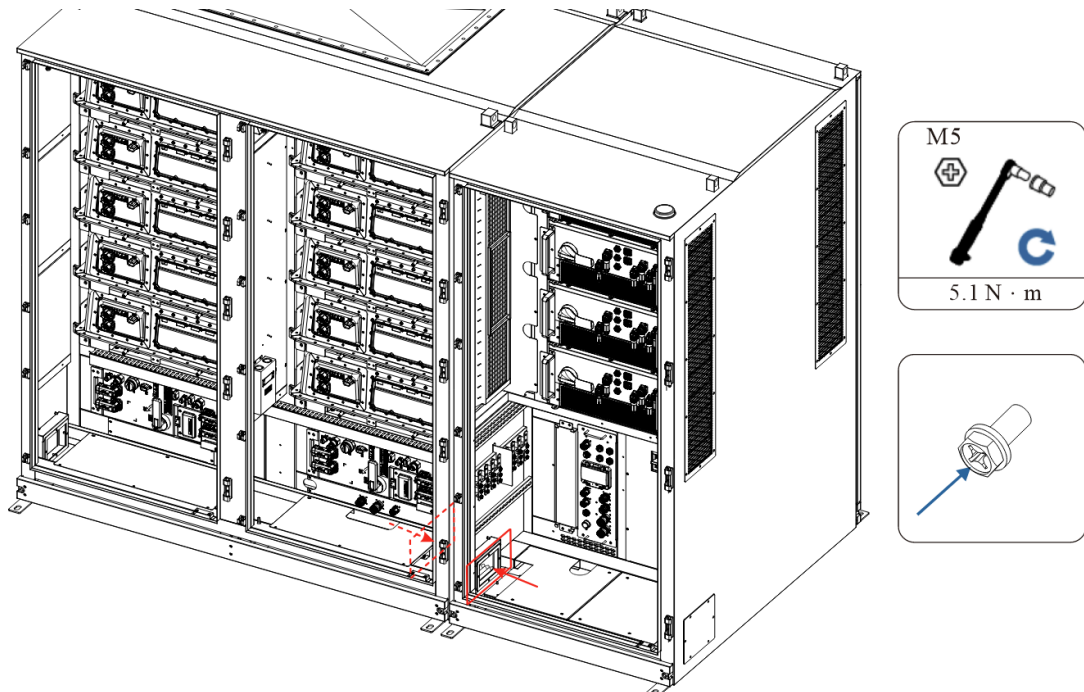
Installieren Sie die Spulendruckplatten
